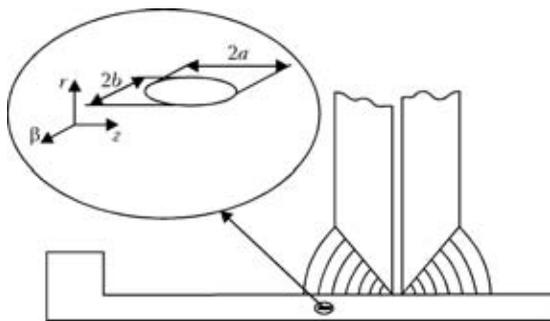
Схема ламелярной трещины в зоне сварного соединения: a, b — габаритные размеры ламелярной трещины
